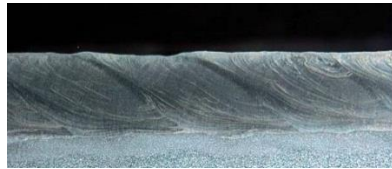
Схема наплавлення на циліндричну поверхню
